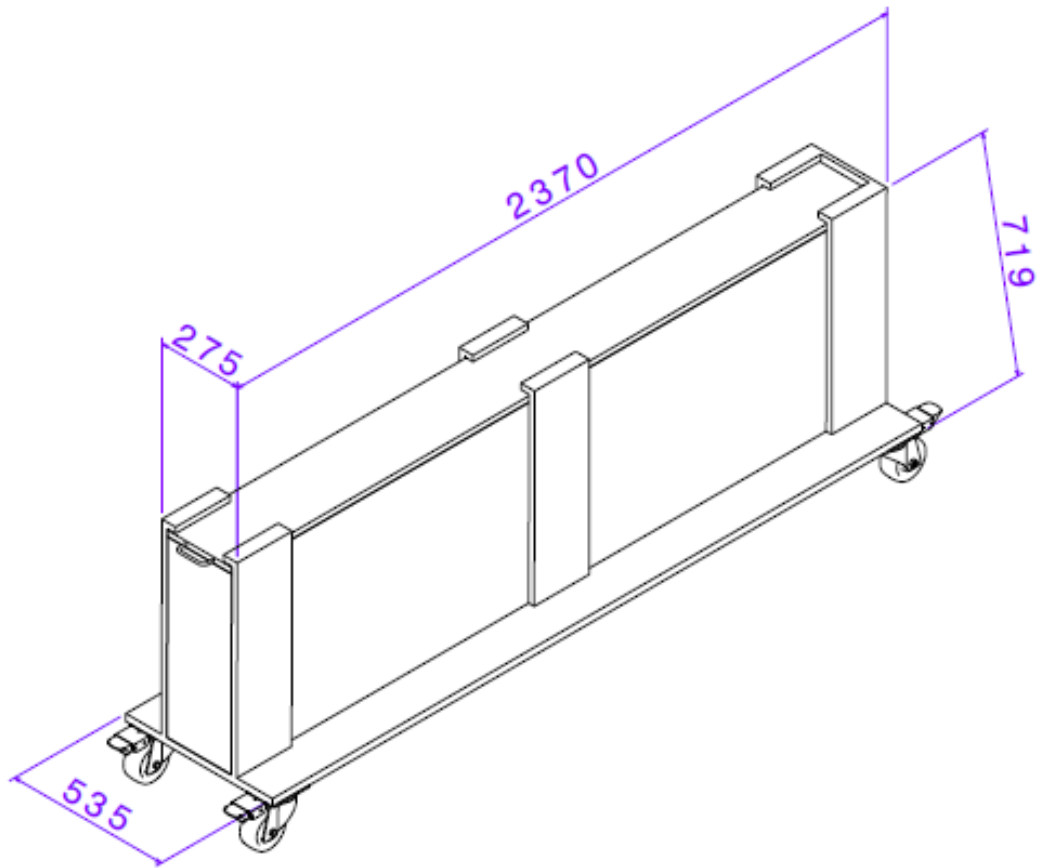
Plano acotado de la caja en mm. Esquema realizado con CATIA V6TM.
